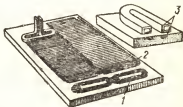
Одновитковый индуктор для закалки плоской поверхности непрерывно-последовательным способом:
